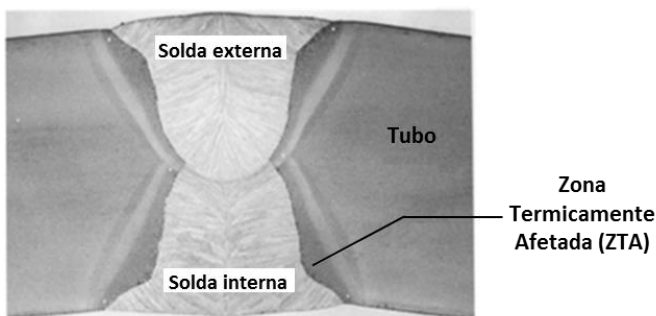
Macrografia da solda SAW de um tubo UOE.
